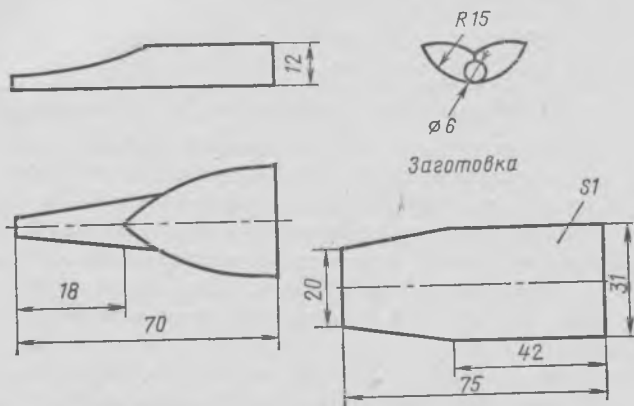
Приспособления для сбора сока из пней полузакрытым способом
